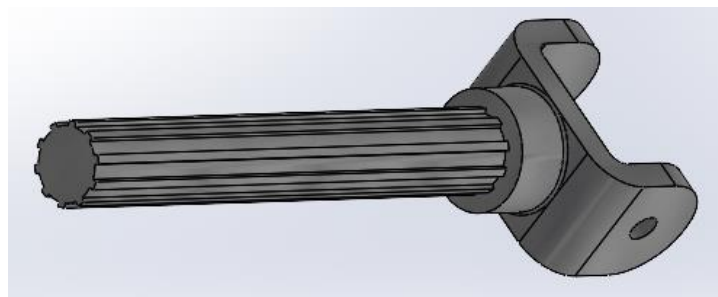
Árbol de transmisión fijo de la junta cardán en SolidWorks.
